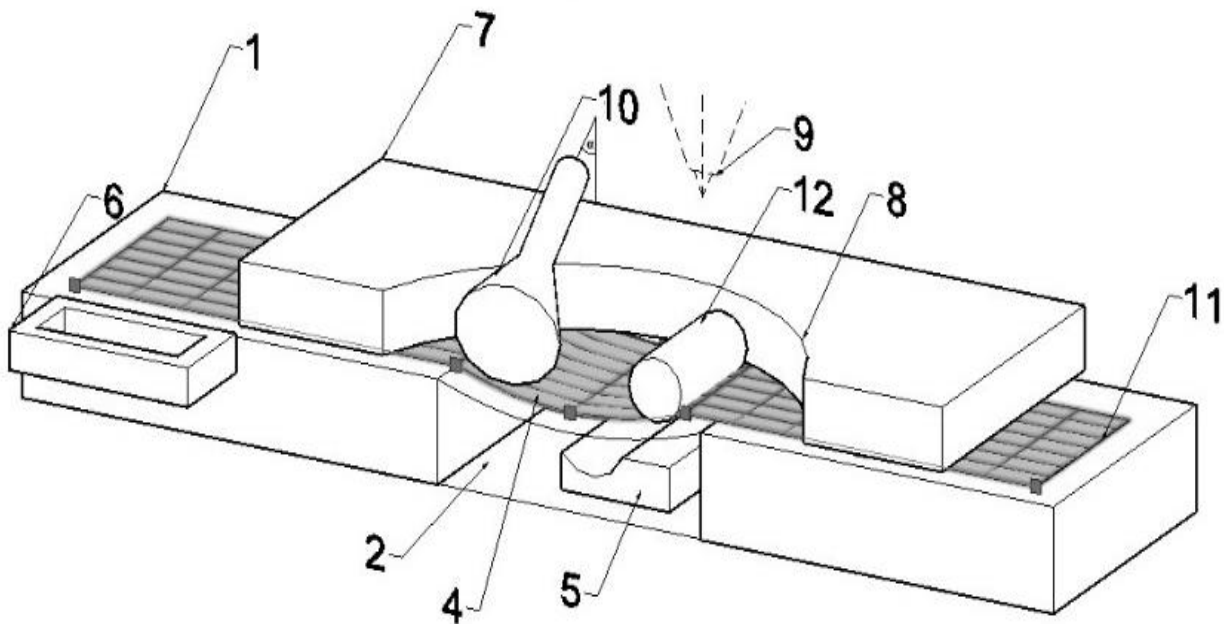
Схема пристрою для наплавлення плоских тонкостінних деталей (рух заготовки – зліва направо)
